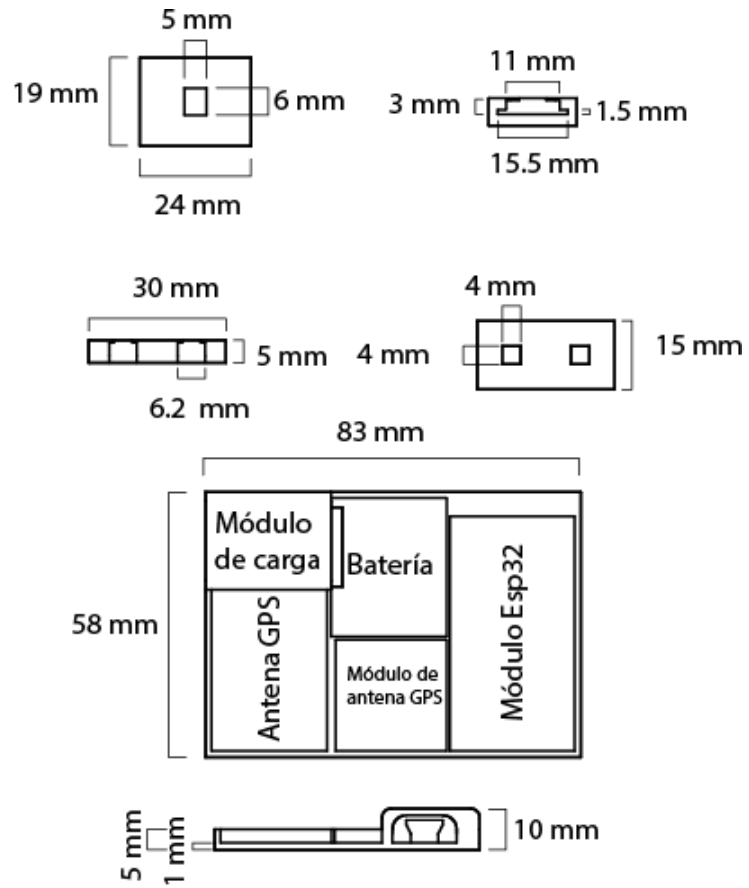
Planos de cubierta para los dispositivos electrónicos.
